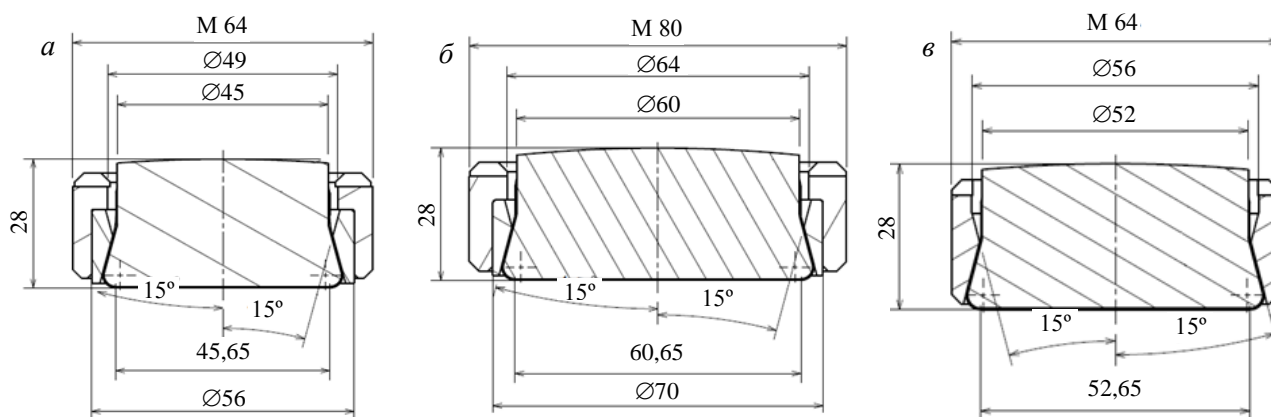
Типоразмеры КЭИН: а — тип А; б — тип Б; в — тип С
